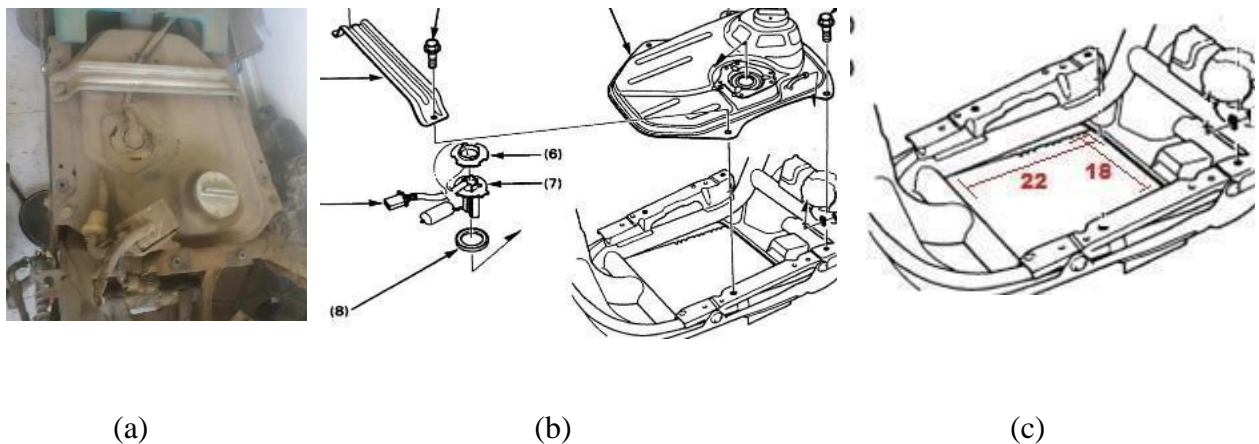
Tanque de combustible; Fuente [24] [E.P]
